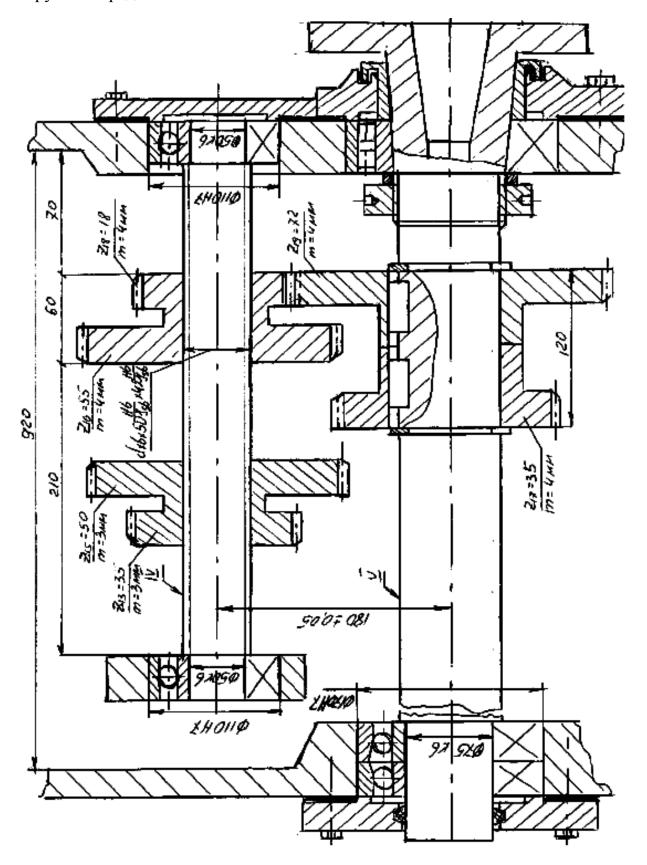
Сборочный чертеж наиболее нагруженной группы передач
